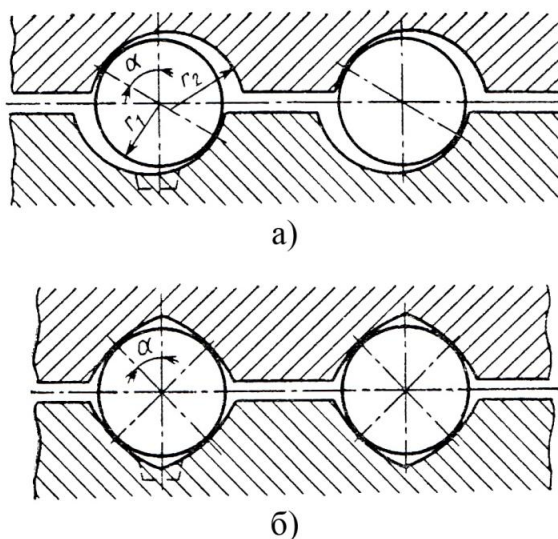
Профили резьбы шариковых пар винт-гайка
